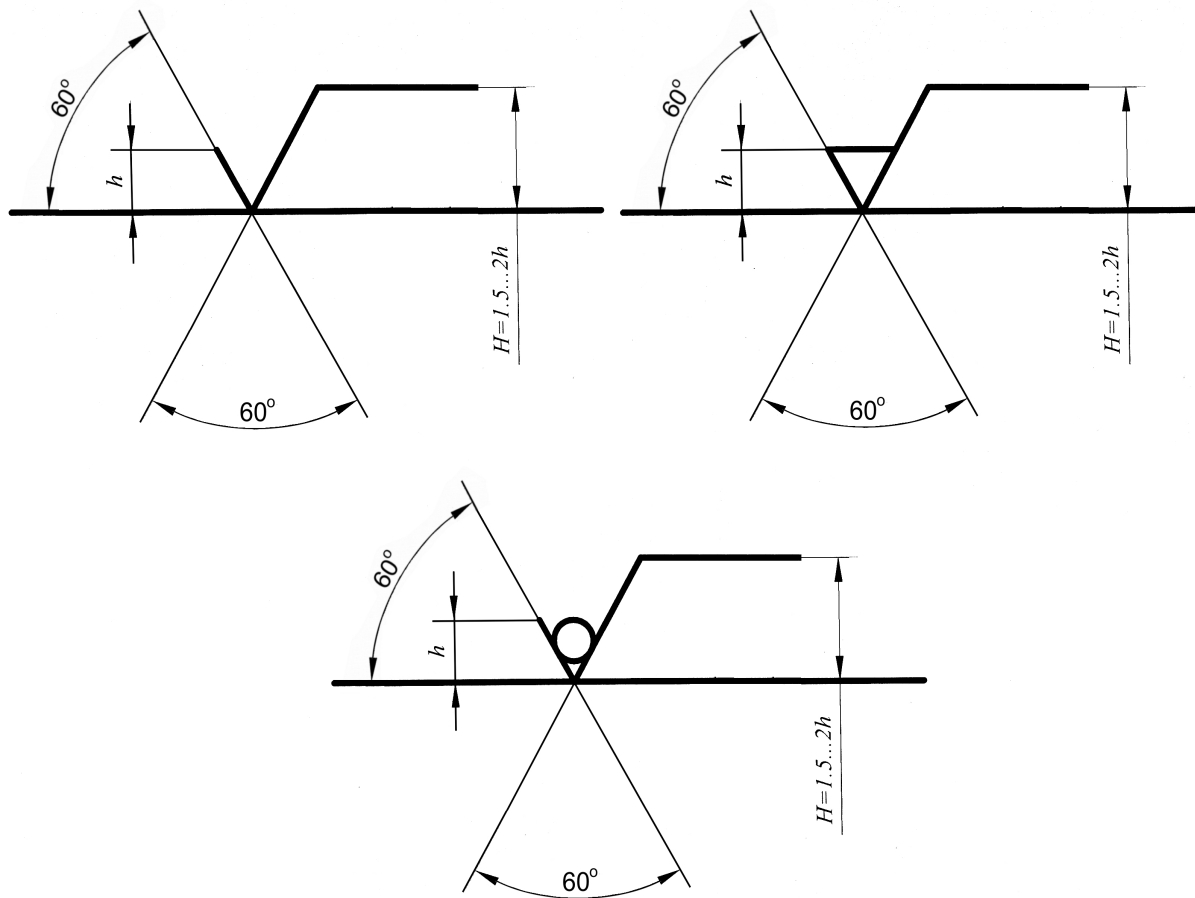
Знаки обозначения шероховатости поверхности
